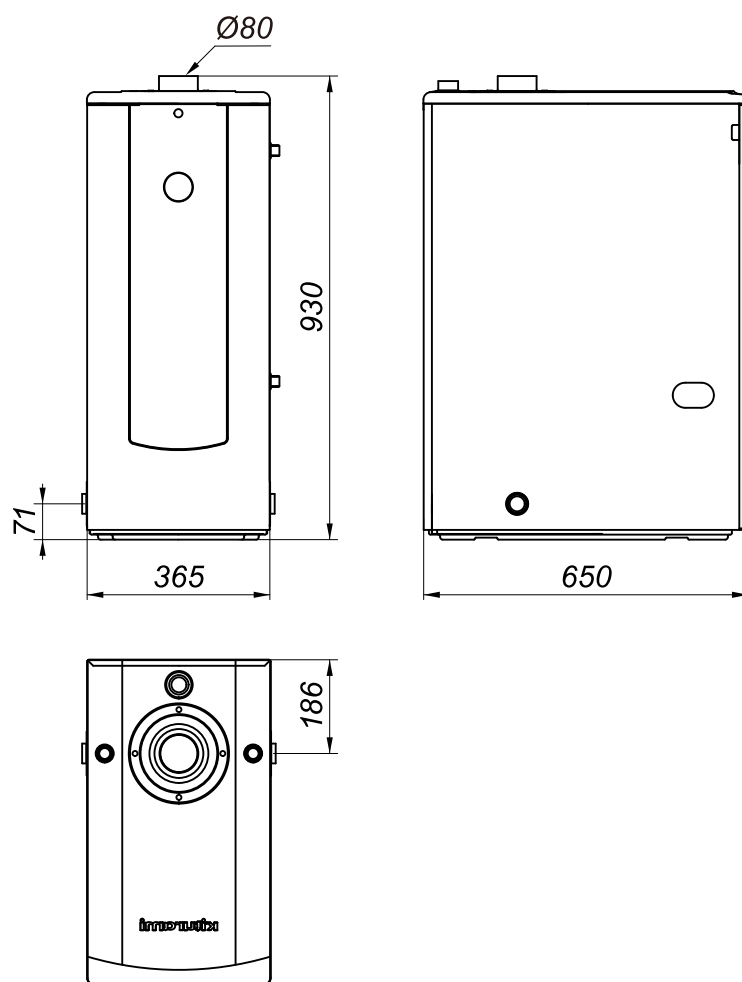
Габаритные размеры Turbo 15/20/24/35.
